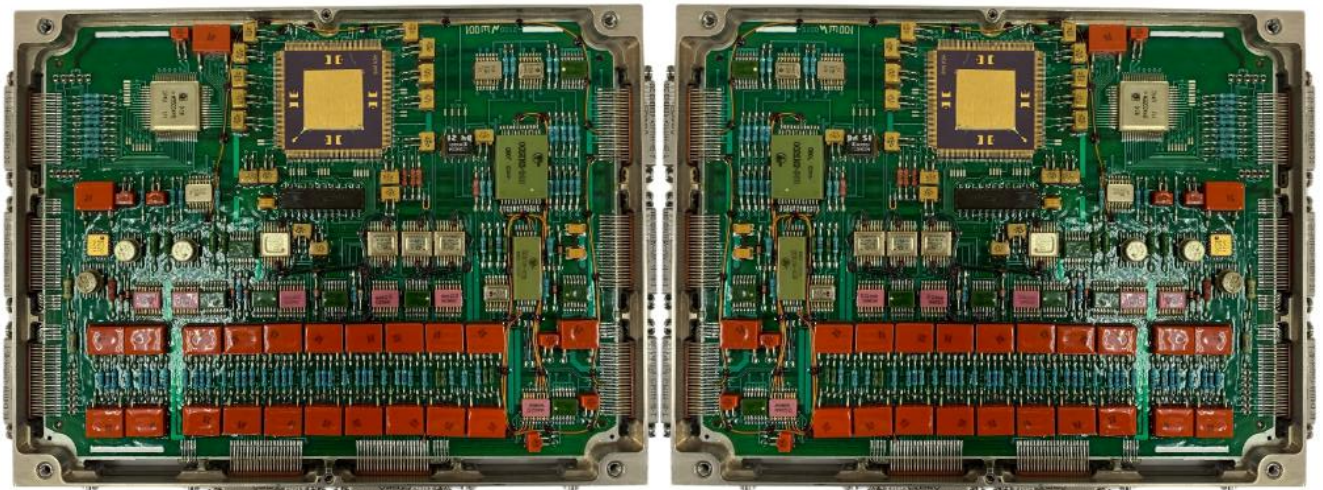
Фотографии резервируемой и резервной ПП
